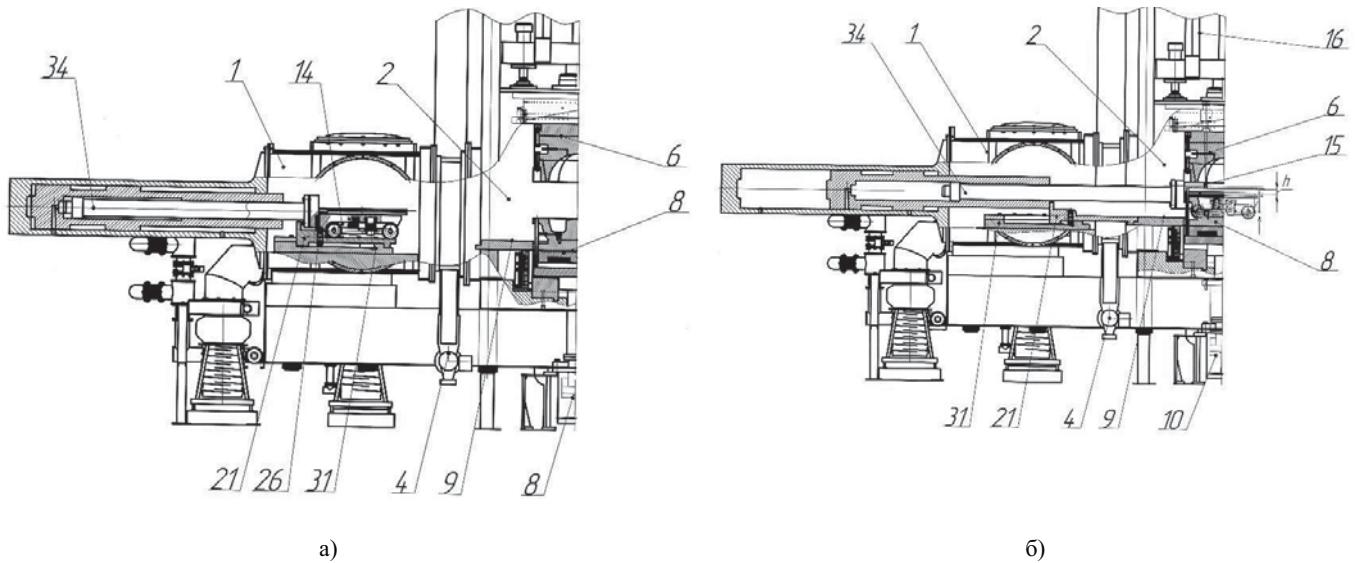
Перемещение каретки вместе с опорной плитой 20:
